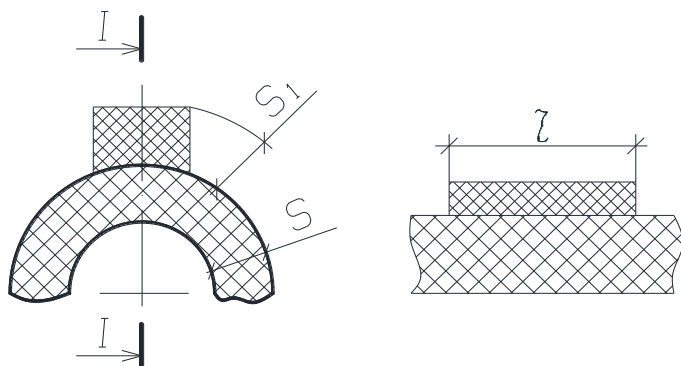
Конструктивные элементы подготовленных кромок (швы Н4)
